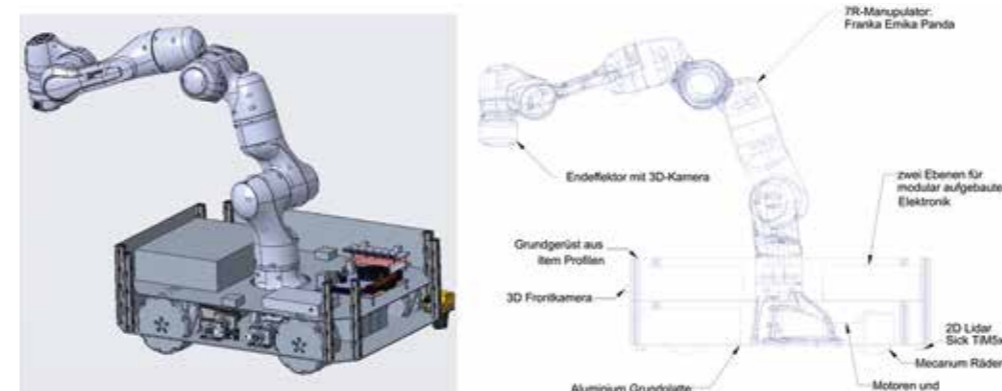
Roboter 3D Konstruktionszeichnung (links), Beschreibung des modularen Aufbaus der Roboterplattform (rechts)
